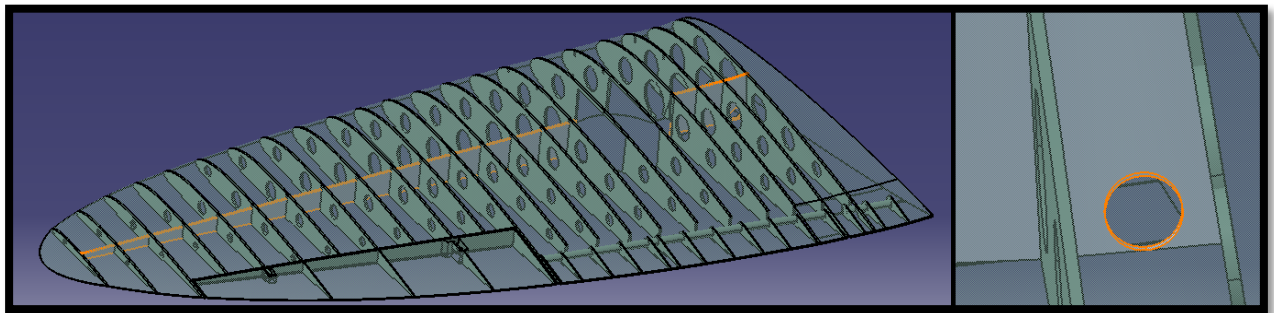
Ala: largueros y detalle del agujero que evita la colisión con un componente el tren de aterrizaje
